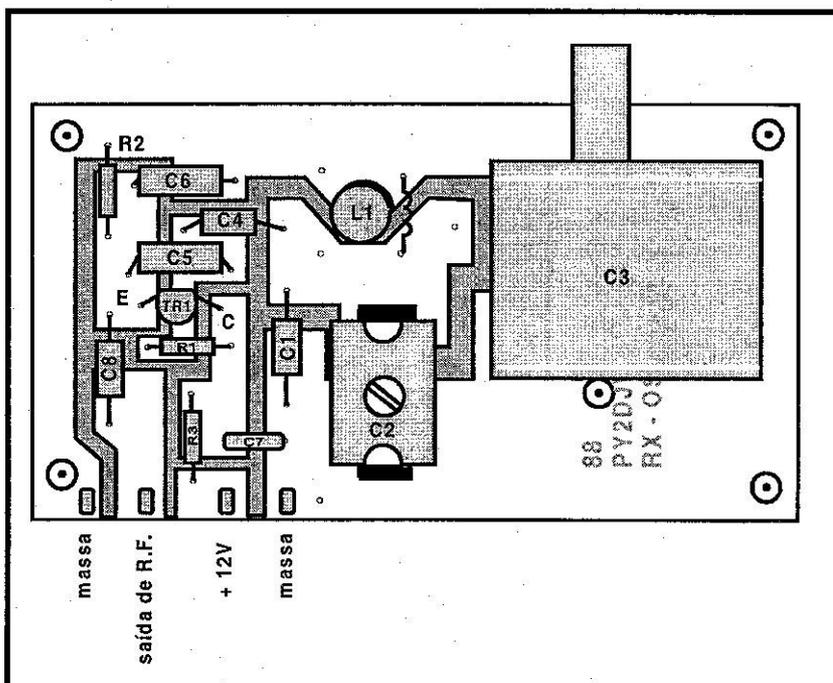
Disposição dos componentes sobre a placa de circuito impresso da Fig. 3.
